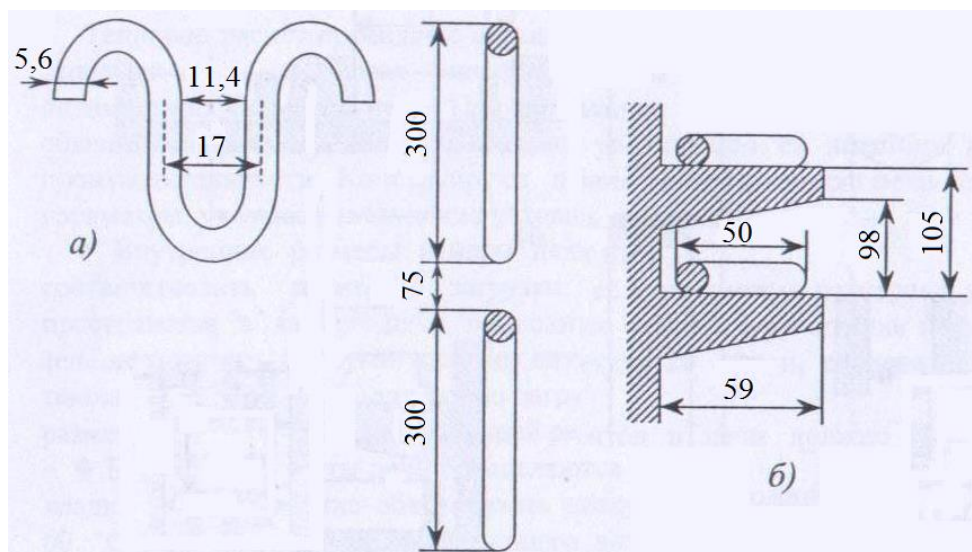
Проволочный зигзагообразный нагреватель: а) общий вид; б) проволочный зигзаг на полочке
